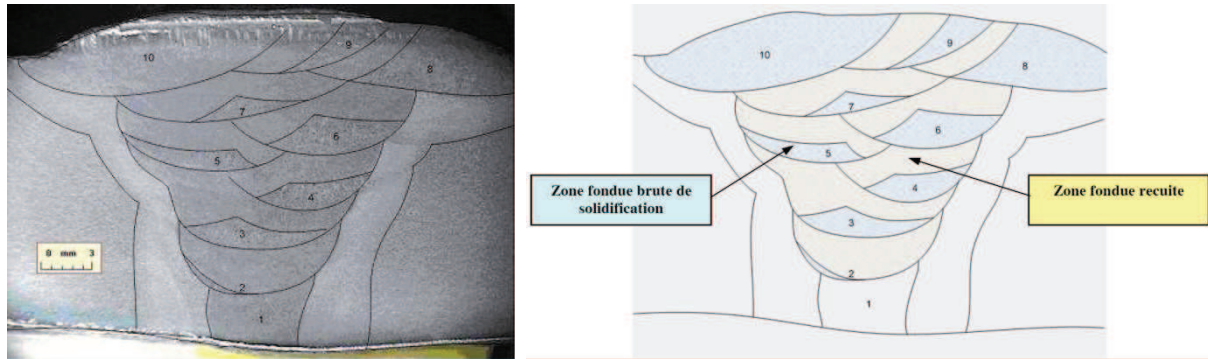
ZFBS et ZFR dans un joint soudé en acier ferritique TU42C [LEC 06]
